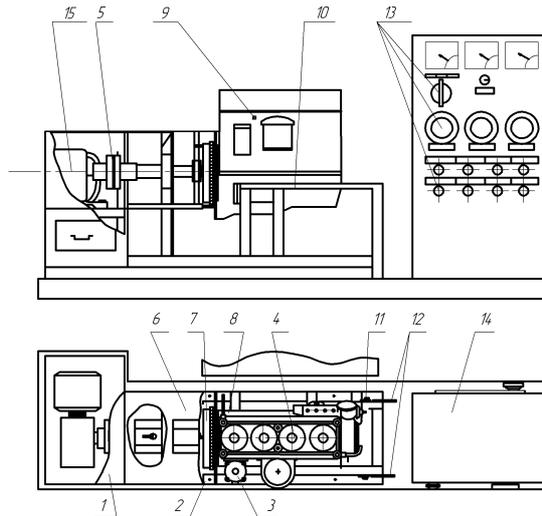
Общий вид стенда для реализации триботехнологии совместной трехфазной приработки основных сопряжений двигателя: 1 – приводная станция; 2 – фиксатор; 3 – фильтр; 4 – гильза цилиндров; 5 – муфта; 6 – защитный щиток; 7 – маховик двигателя; 8 – основание для двигателя; 9 – двигатель, подвергаемый приработке; 10 – рамка специальная; 11 – токоподвод на блок; 12 – токоподводы на шатуны (общая шина) и коленчатый вал; 14 – шкаф управления; 15 – редуктор.
